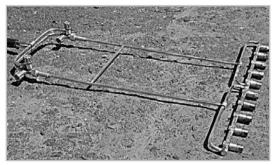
Горелка для нагрева рельсов ГЗУ6-ЖД
